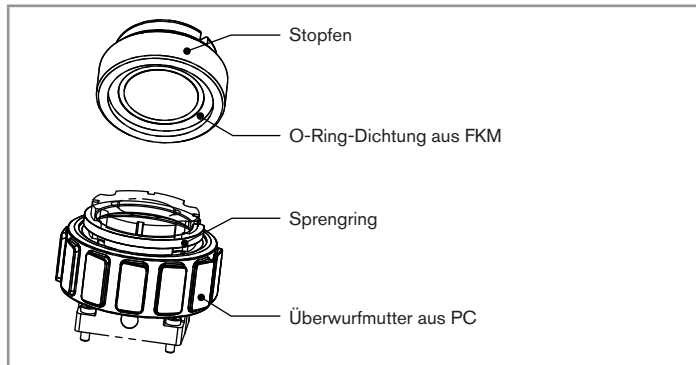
Stopfen mit O-Ring-Dichtung, Befestigungsmutter und Sprengring
